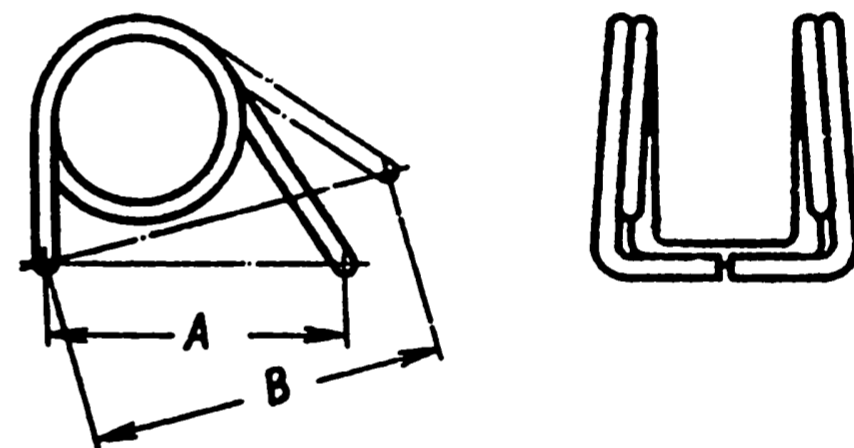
Схема проверки пружины рычага: А - размер в свободном состоянии; В - размер под нагрузкой
